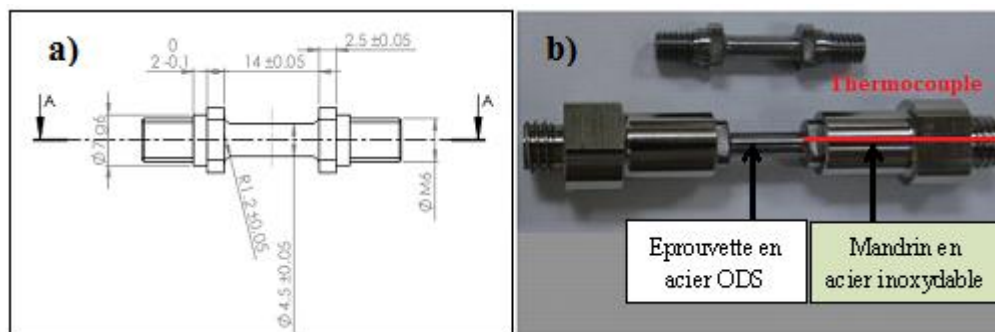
Éprouvette de torsion : a) géométrie, b) montage expérimentale de la mini-éprouvette.
